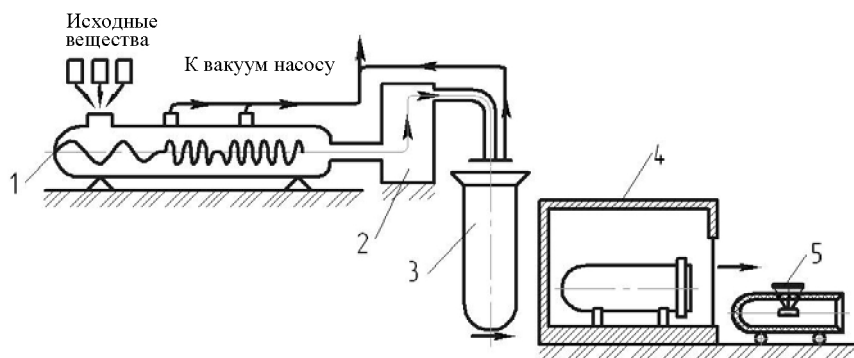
Схема изготовления заряда смешанного топлива непрерывным способом:
